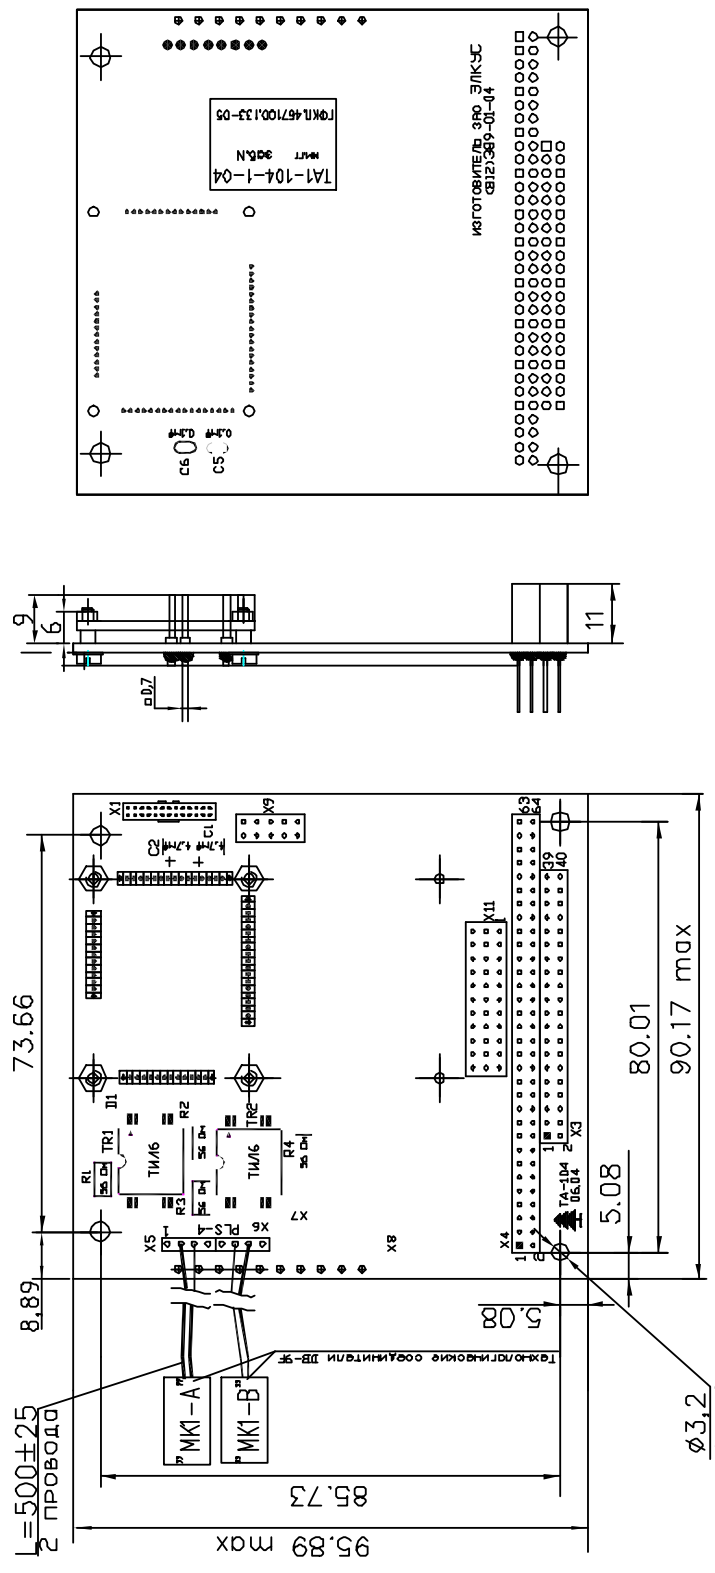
Габаритный чертеж исполнения ТА1-104-1-03
